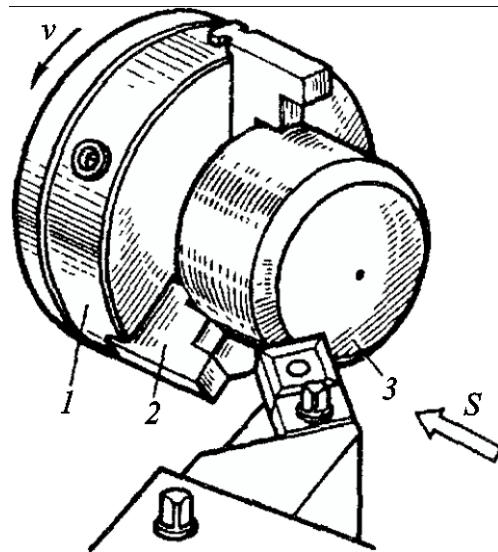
Закріплення заготовки у перевернутих кулачках патрона:
